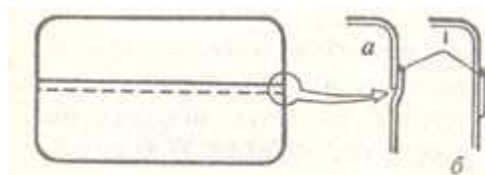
Сковорода из двух кастрюль. Соединение половинок: а — вхождением одной в другую; б - с кольцом (1 - места сварки).
